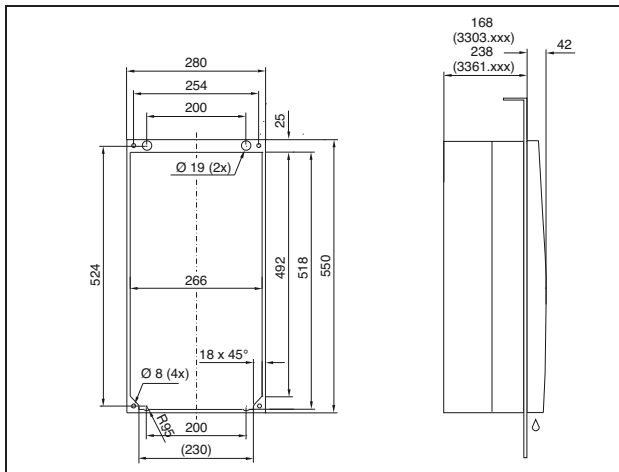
3303.xxx, 3361.xxx komplett inbyggnad
